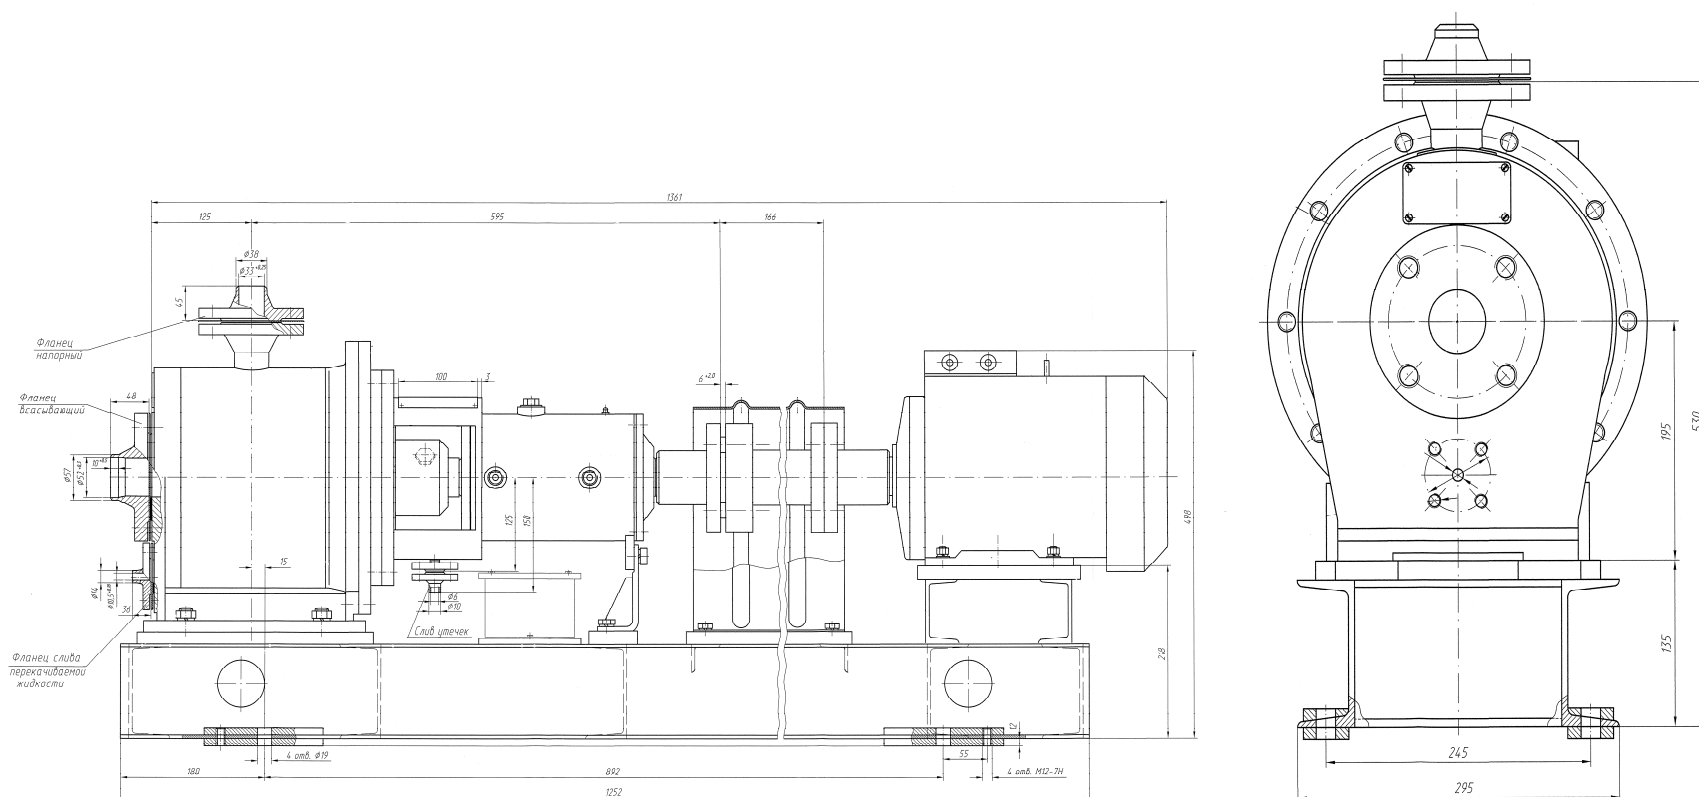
Габаритный чертеж насосного агрегата типа ЦНА 12,5/50
